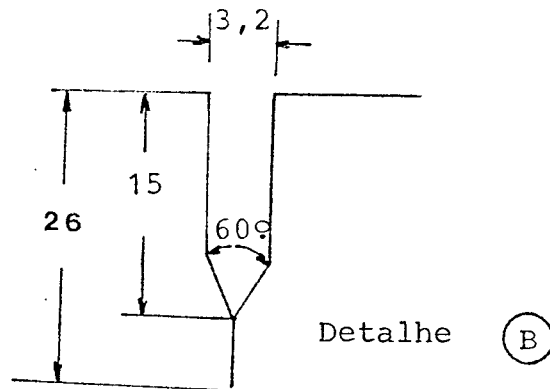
Dimensões dos corpos-de-prova para os ensaios COD e Integral J
